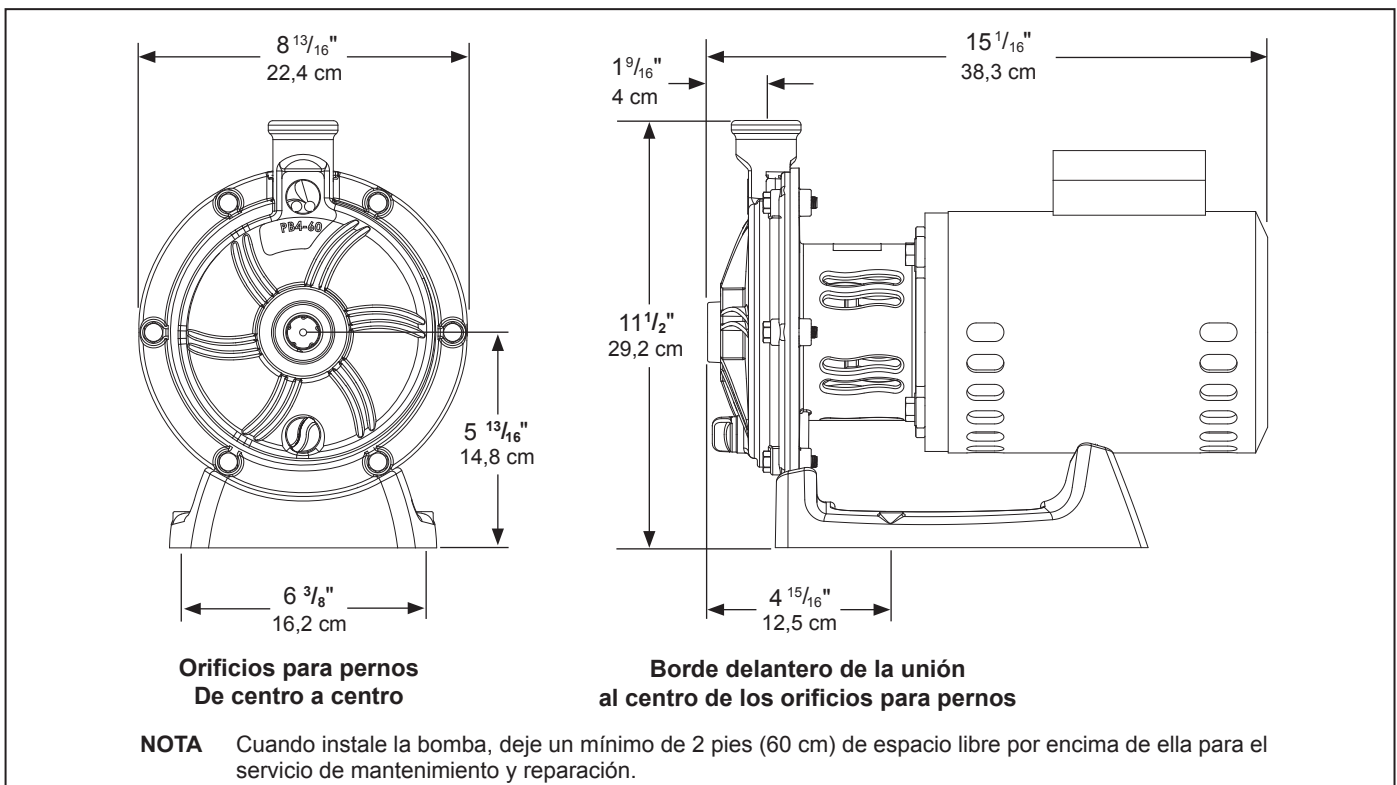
Dimensiones de la bomba Polaris reforzadora PB4-60
